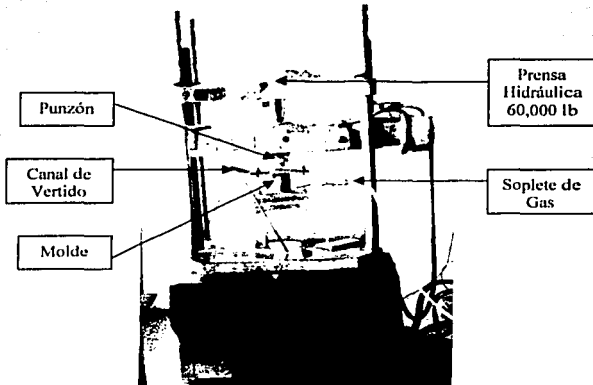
Montaje del molde, botador y punzón en la prensa hidráulica
